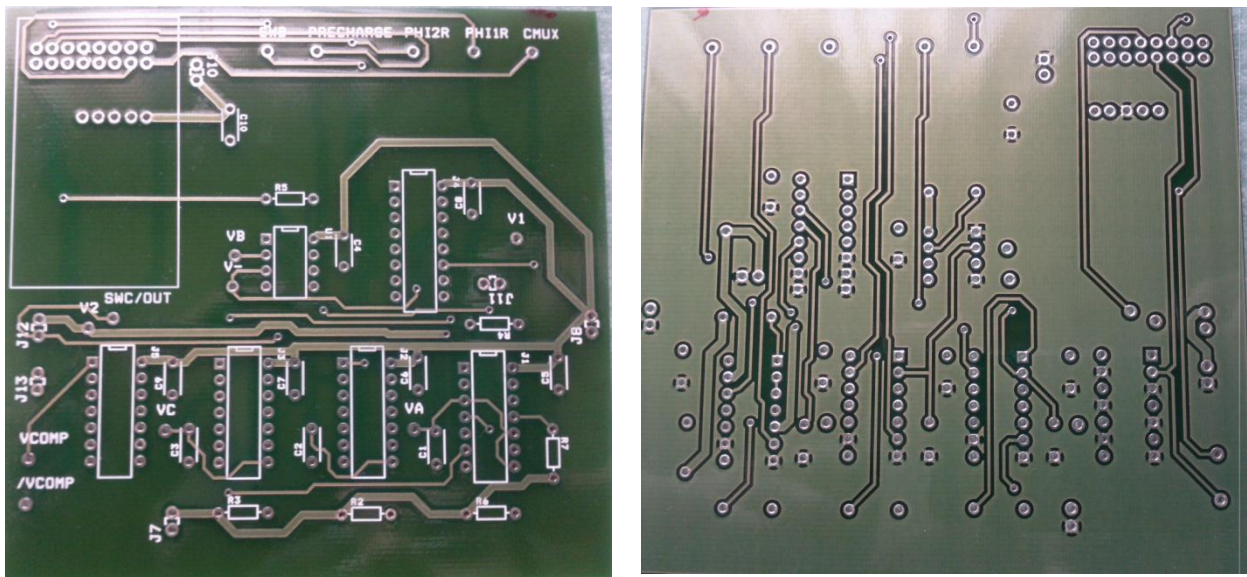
Capas TOP (izquierda) y BOTTOM (derecha) de la PCB fabricada.
